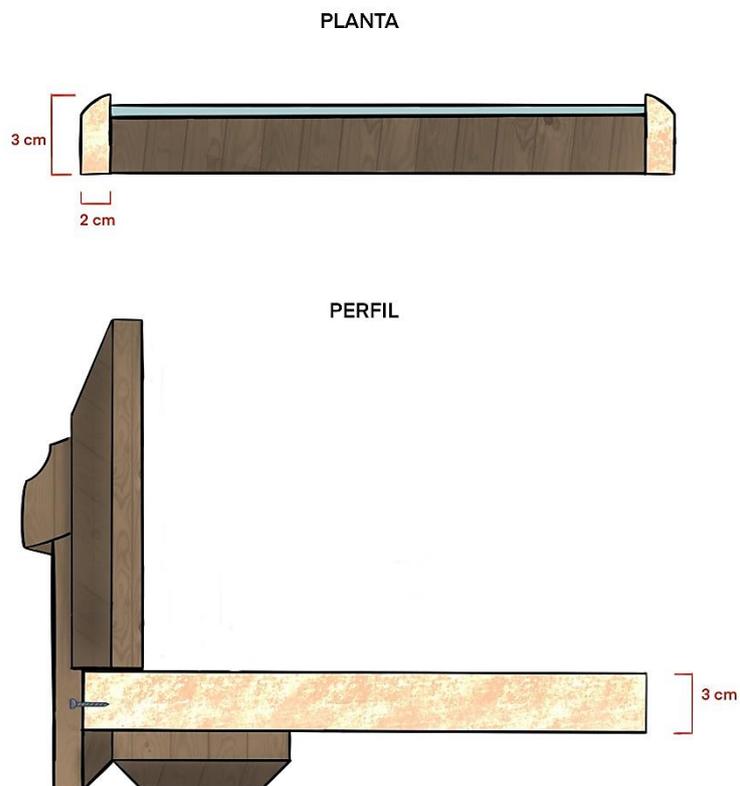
Croquis planta y perfil de la propuesta del enmarcado.
